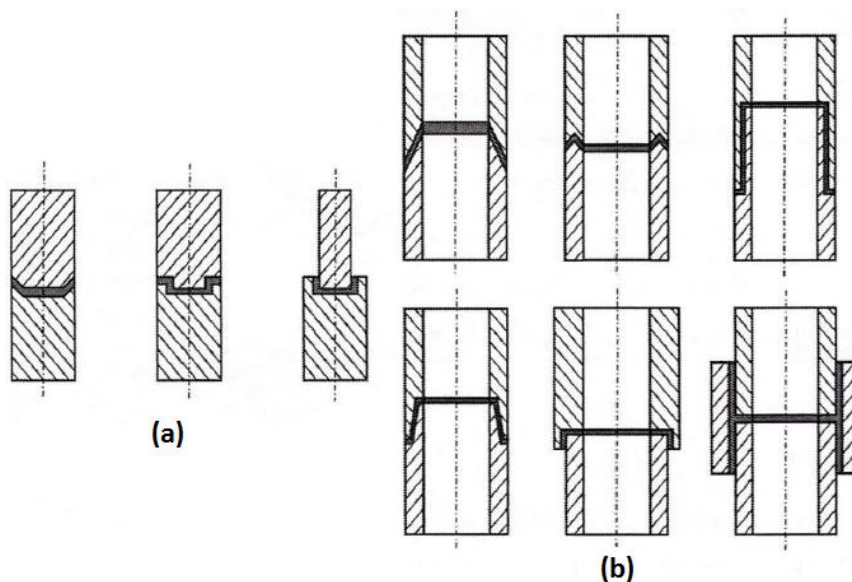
Exemplos de juntas cilíndricas: (a) juntas para varões e (b) juntas para tubos [14].
